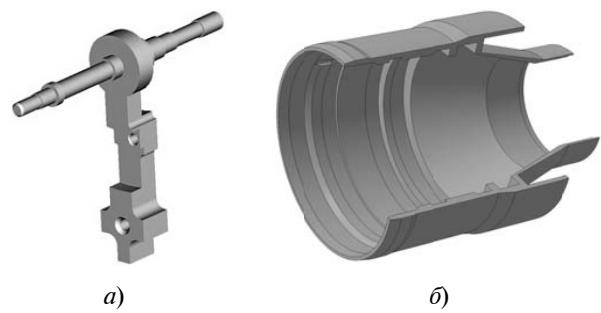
Конструкция деталей с высокой точностью размеров (а) и взаимного расположения поверхностей (б)
